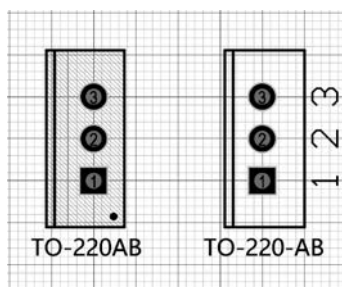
PCB 设计中的 TO-220AB 与 TO-220-AB 封装
